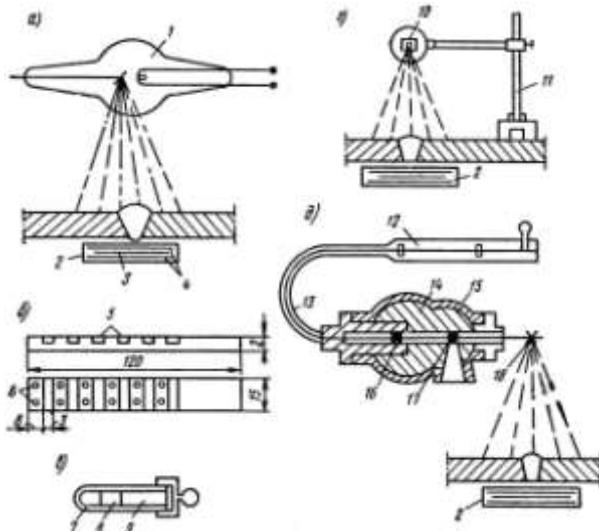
Контроль сварных соединений просвечиванием
